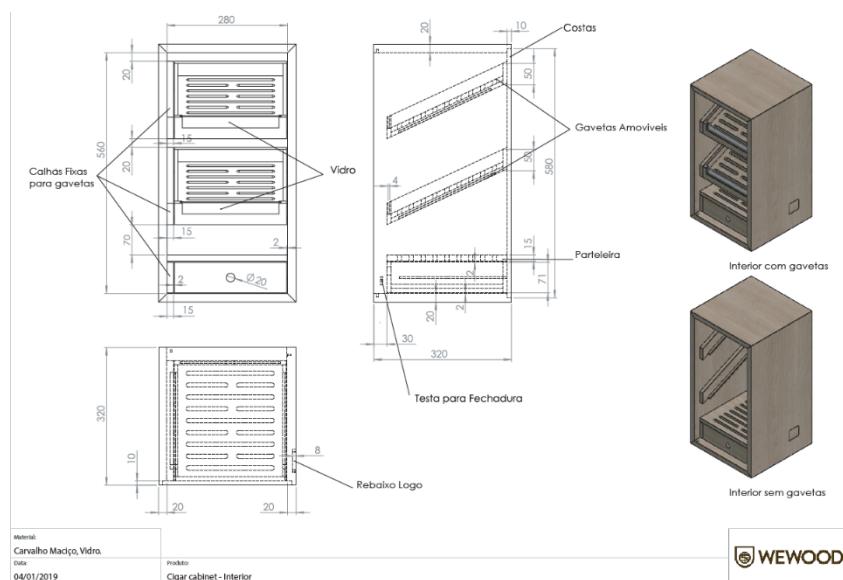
Expositor de charutos, desenho técnico. Fonte: Autor.
